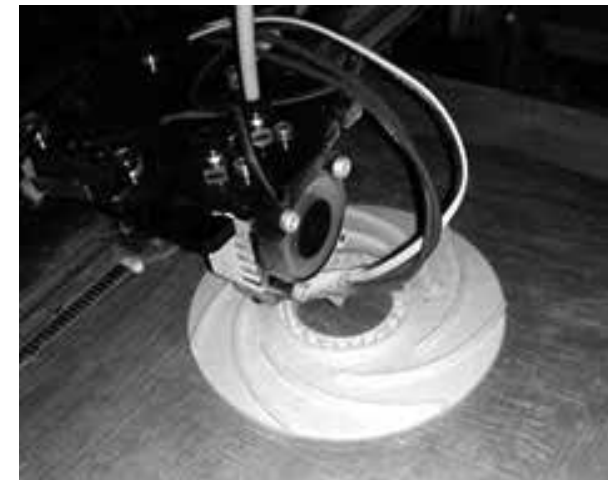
Виготовлення прототипу робочого колеса за допомогою технологій 3D друку.
